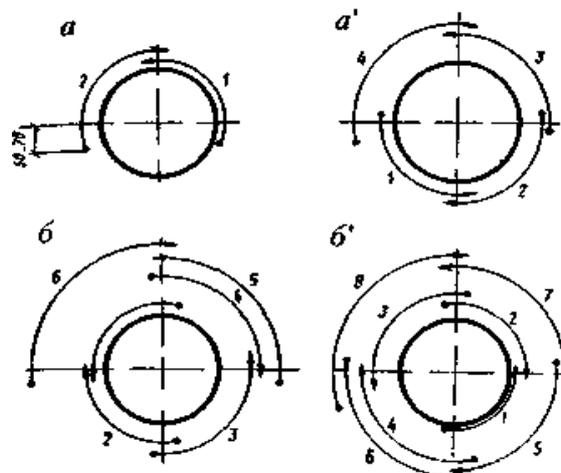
Сварка стыков с поворотом трубы на 180°:
